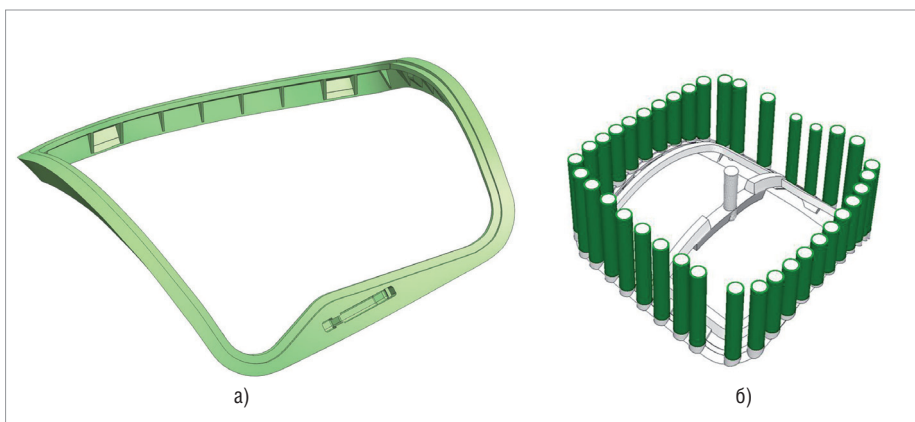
Конструкция ЛПС, применяемая на предприятии при изготовлении отливок типа "Рама": а) 3D-модель отливки; б) 3D-модель литейного блока
